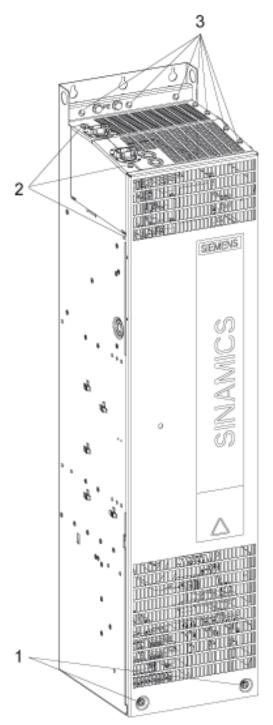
Montaje del Braking Module en un Power Module de tamaño FX: pasos 1 - 3
